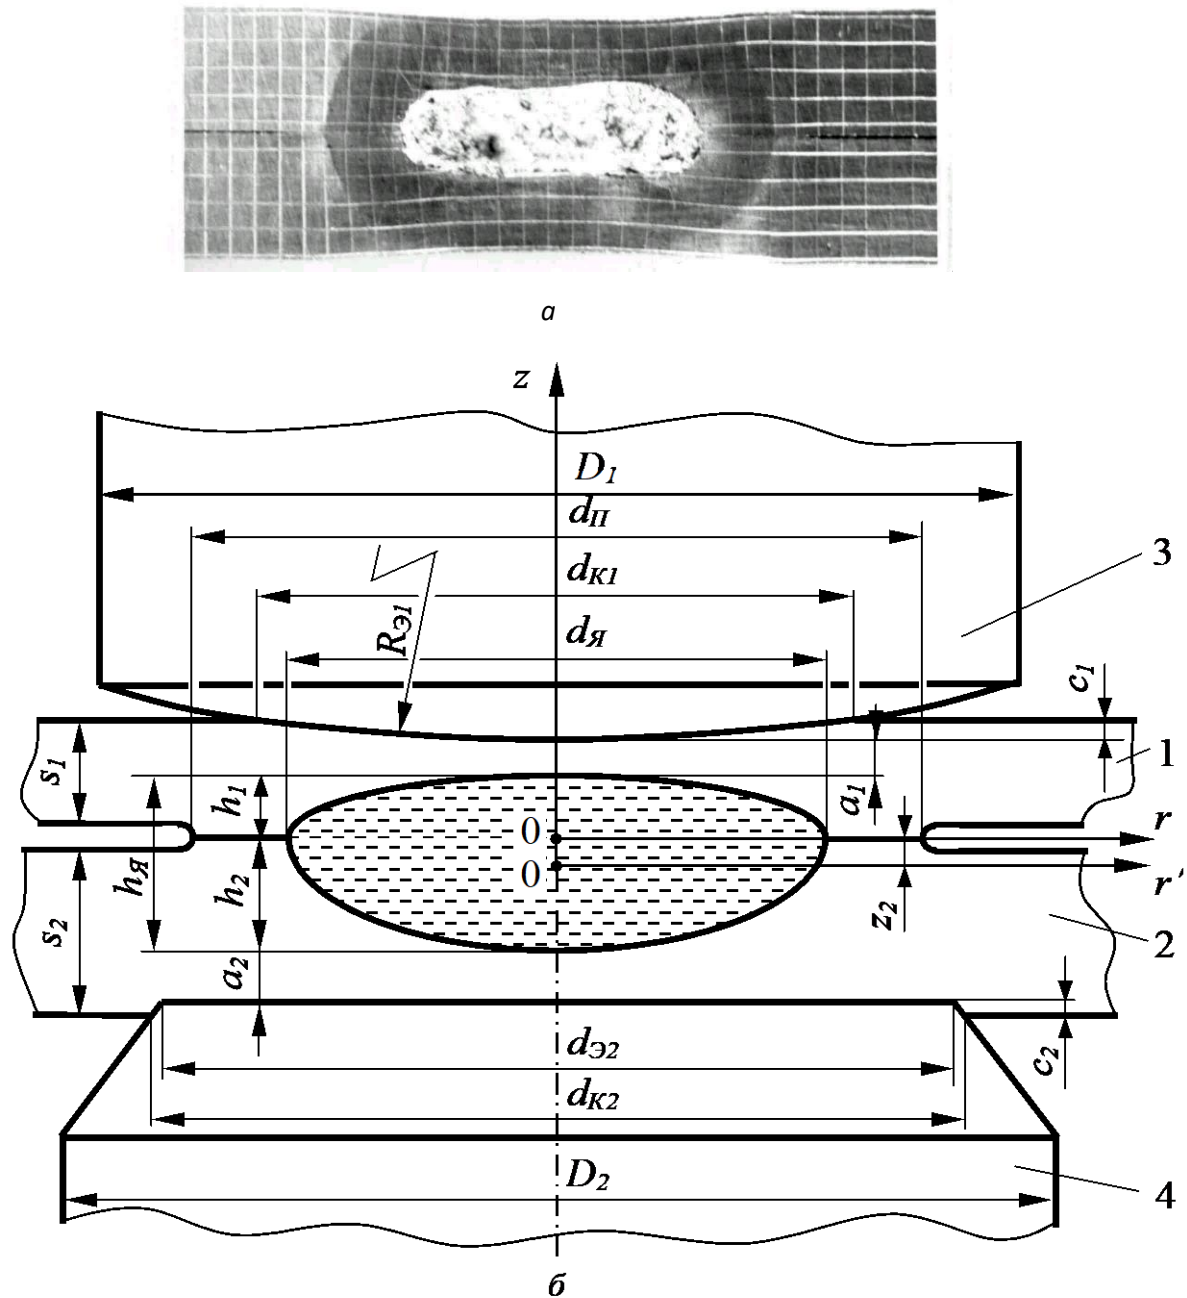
Вид точкового зварного з'єднання (а) та схема геометричних параметрів зварювання деталей 1 і 2 різної товщини електродами зі сферичною 3, плоскою 4 робочими поверхнями:  $s_1, s_2$  – товщина деталі 1 і 2;  $d_Я$  і  $h_Я$  – діаметр і висота ядра розплавленого металу;  $h_1, h_2$  – висота зони розплавлення в деталі;  $c_1, c_2$  – глибина вдавнення електроду;  $a_1, a_2$  – відстань від верхньої точки ядра до поверхні деталі;  $d_П$  – діаметр ущільнюючого поясу;  $D_1, D_2$  – діаметр робочої частини електроду;  $d_{К1}, d_{К2}$  – діаметр контакту електрод-деталь;  $R_{E1}$  – радіус сферичної робочої поверхні електрода 1;  $d_{E2}$  – діаметр робочої поверхні електрода 2
